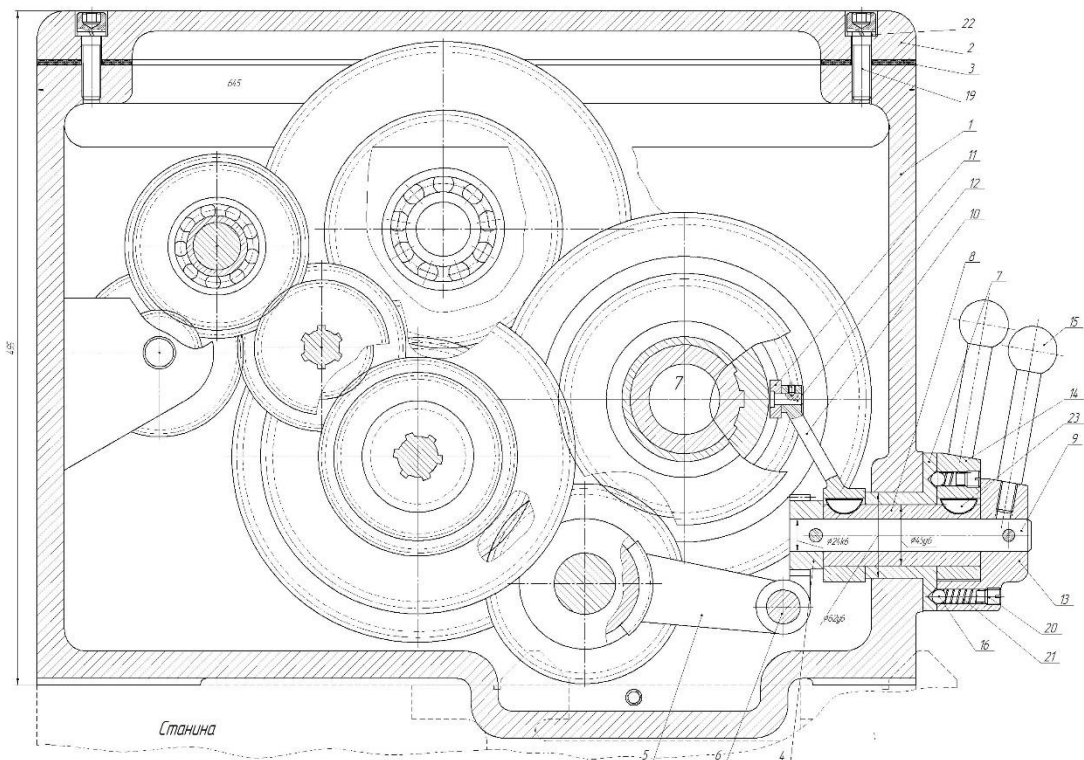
Поперечна компоновка коробки швидкостей токарно-гвинторізного верстату 1А62
